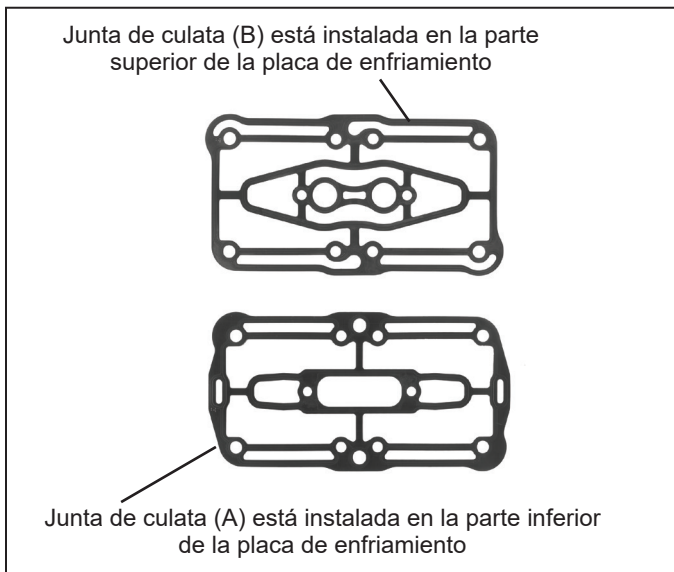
Posición de las juntas de culata del compresor de 720cc Bendix®
